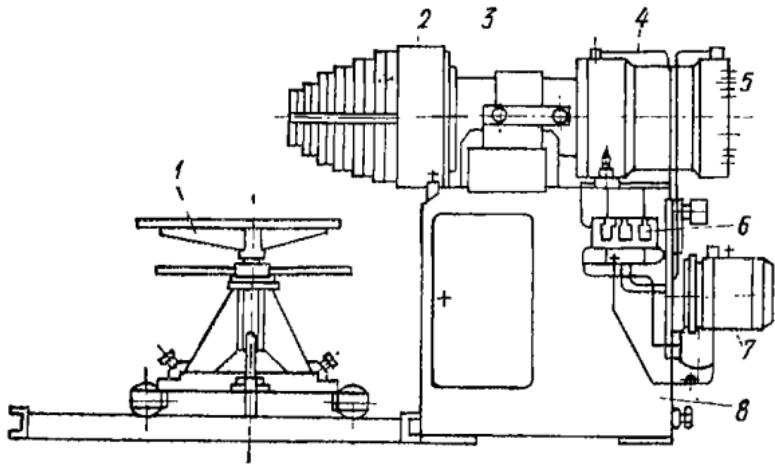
Установка для калибровки труб и деталей трубопроводов:
